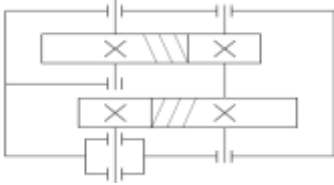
Кинематическая схема соосного двухступенчатого цилиндрического редуктора
